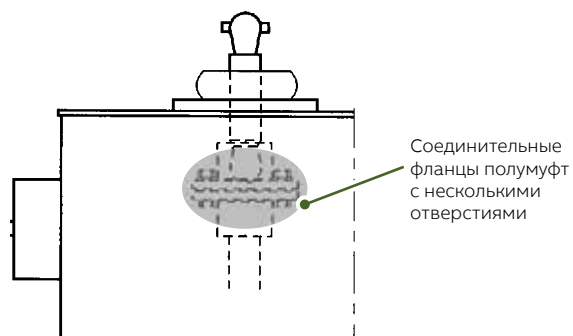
Муфта с несколькими отверстиями механизма BUE
